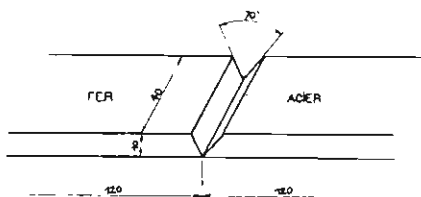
Forme et dimensions de l'éprouvette de pliage.
